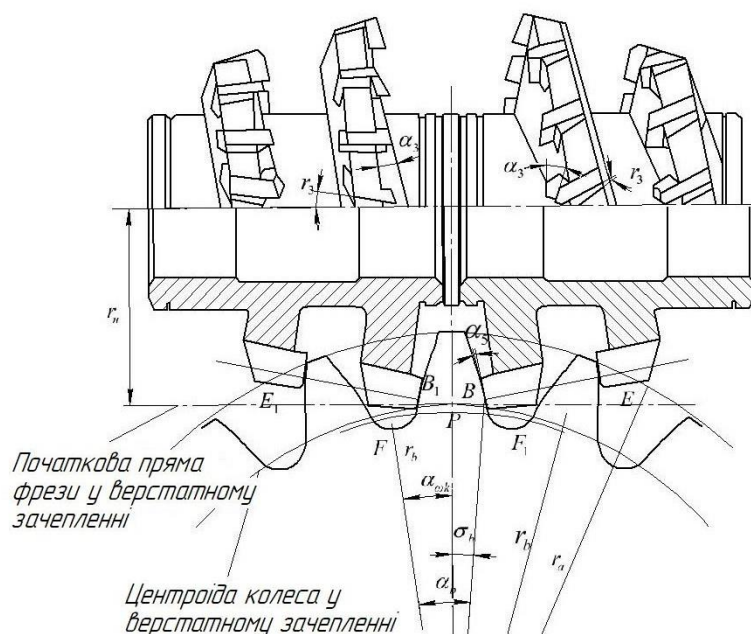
Схема верстатного зачеплення фрези з роздільною схемою формоутворення та оброблюваним зубчастим колесом
